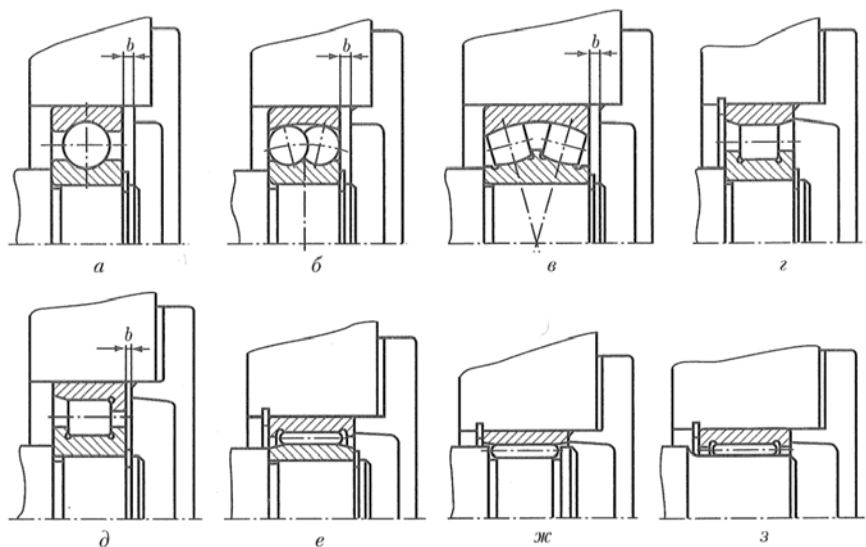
Типы подшипников и схемы их установки в плавающей опоре
